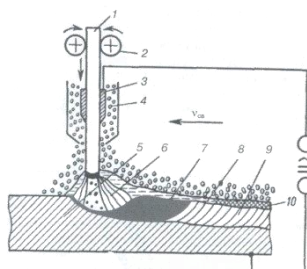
Схема автоматической сварки под слоем флюса:
